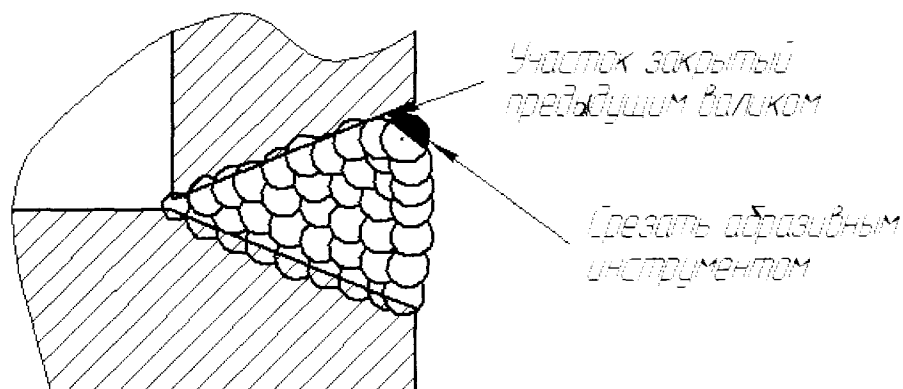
Техника сварки верхнего слоя горизонтального шва
